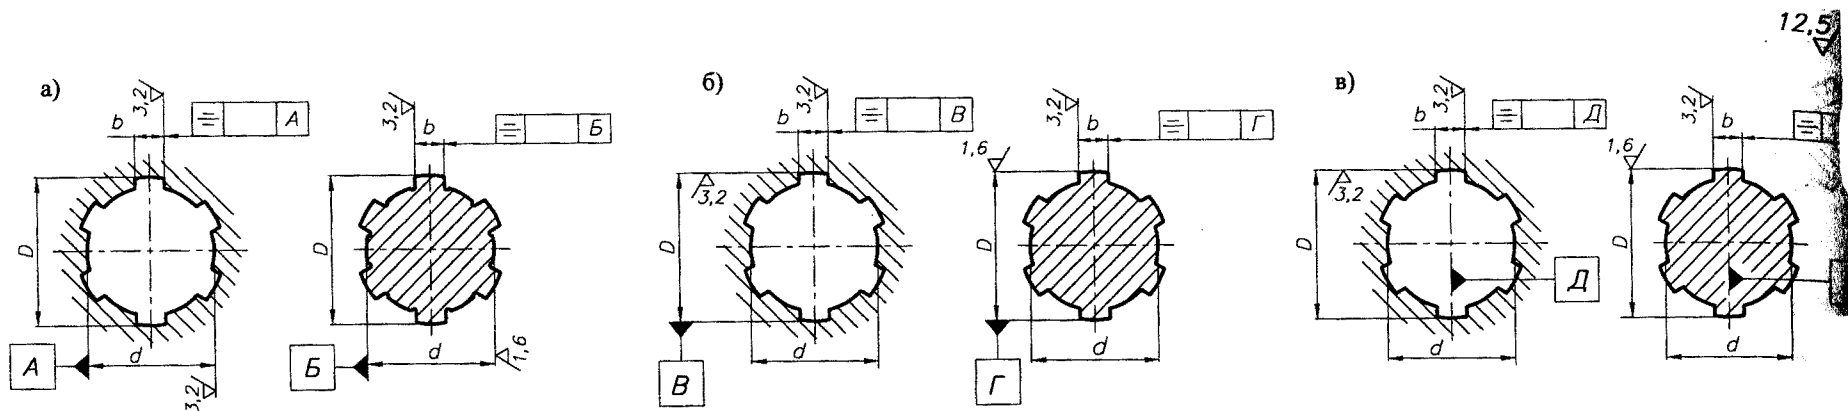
Базовые поверхности, шероховатость, допуски формы и расположения поверхностей шлицевого прямобоочного соединения при центрировании
